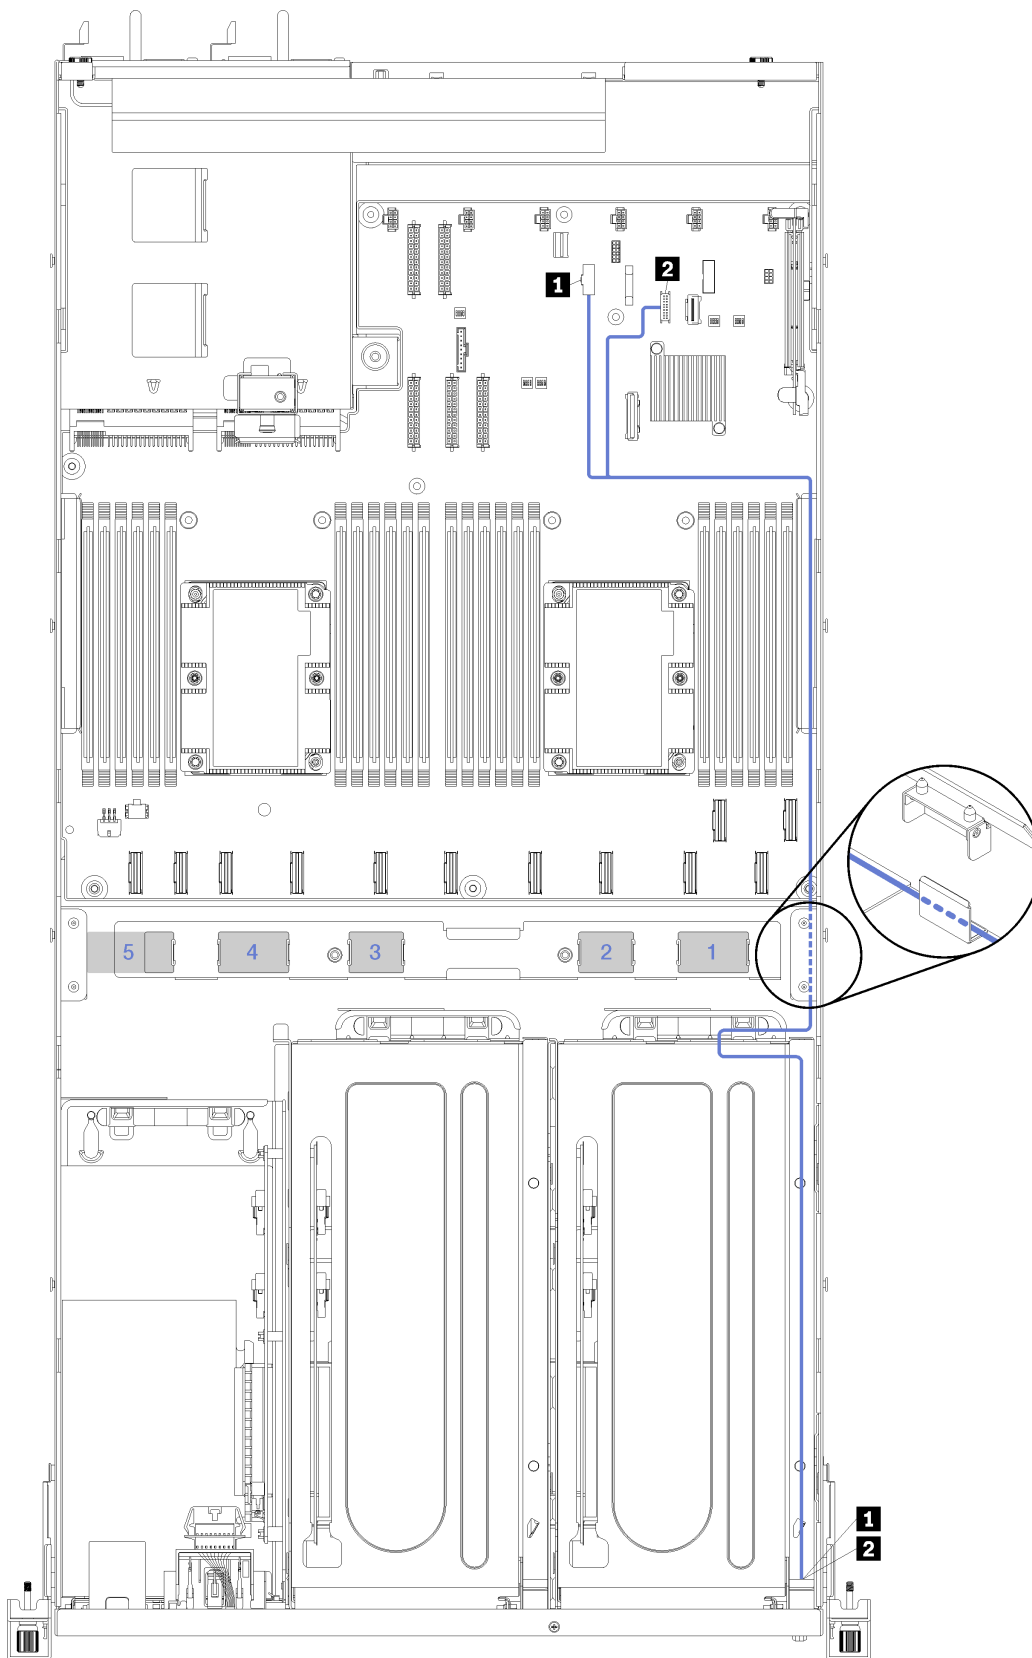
Kabelführung für die Bildschirm- und USB-Kabel
